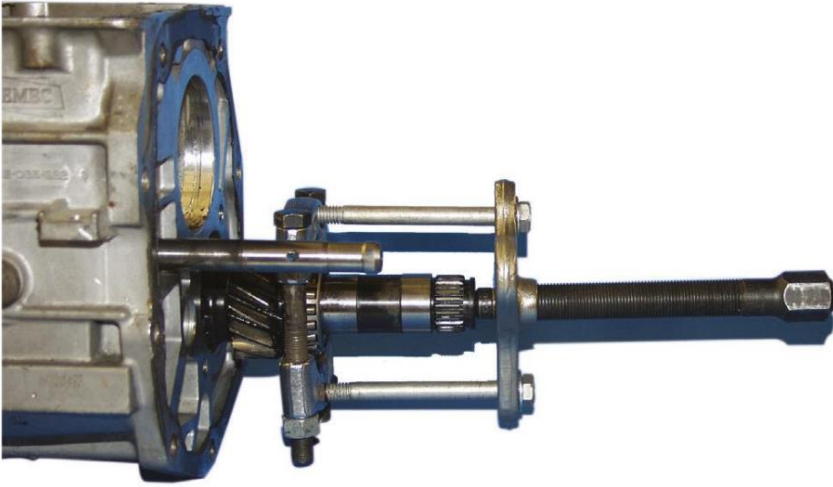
Un cojinete trasero que se quita utilizando un extractor de engranajes/cojinetes.
